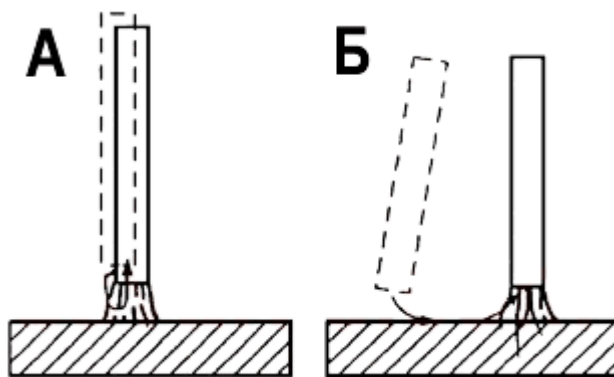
Зажигание дуги при ручной дуговой сварке
